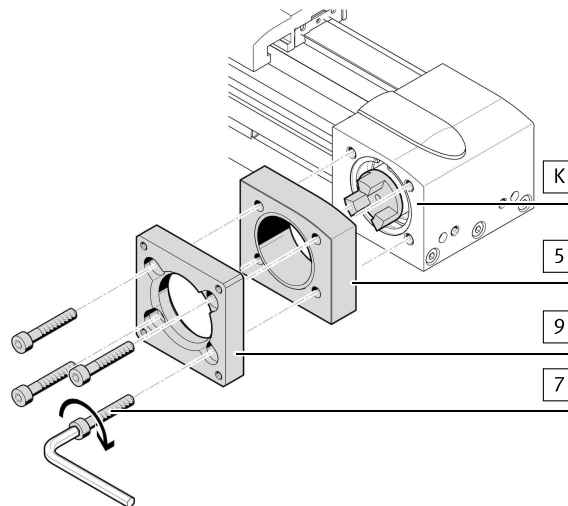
Крепление фланца мотора и корпуса муфты – Вариант В
